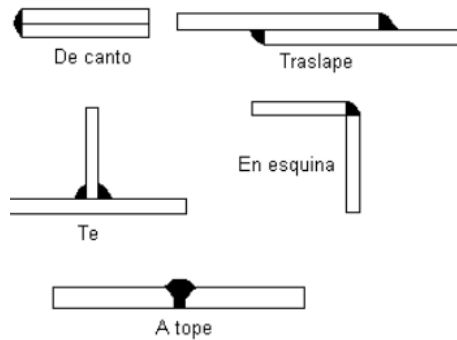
Tipo de juntas de la Soldadura
